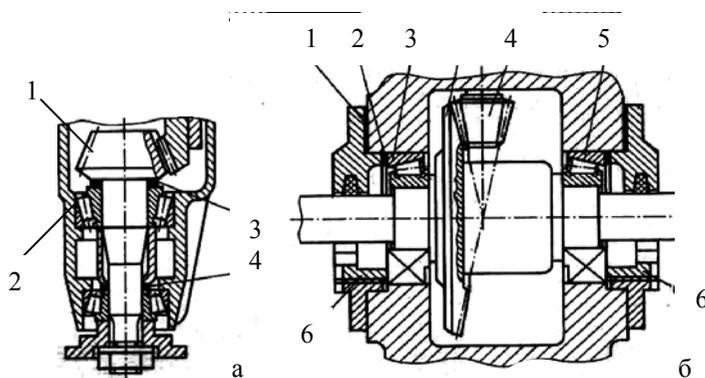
Схемы установки ведущего колеса конической зубчатой передачи с регулированием предварительного натяга подшипников (а) и регулирование ведомого колеса (б), где
